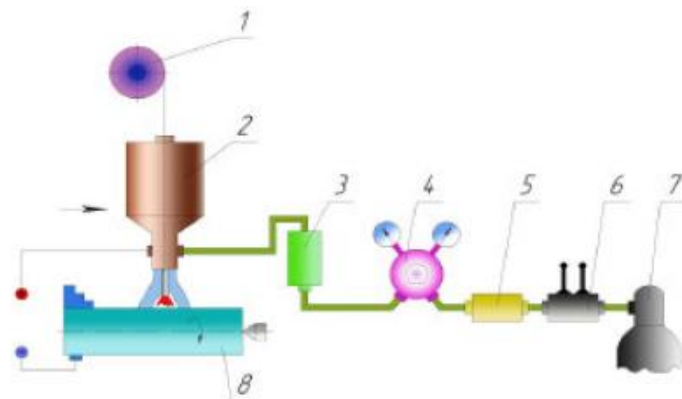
Схема установки для дугового наплавлення в середовищі CO_2 : 1 – касета з дротом; 2 – наплавна головка; 3 – витратомір; 4 – редуктор; 5 – осушувач; 6 – підігрівач; 7 – балон із вуглекислим газом; 8 – деталь.
